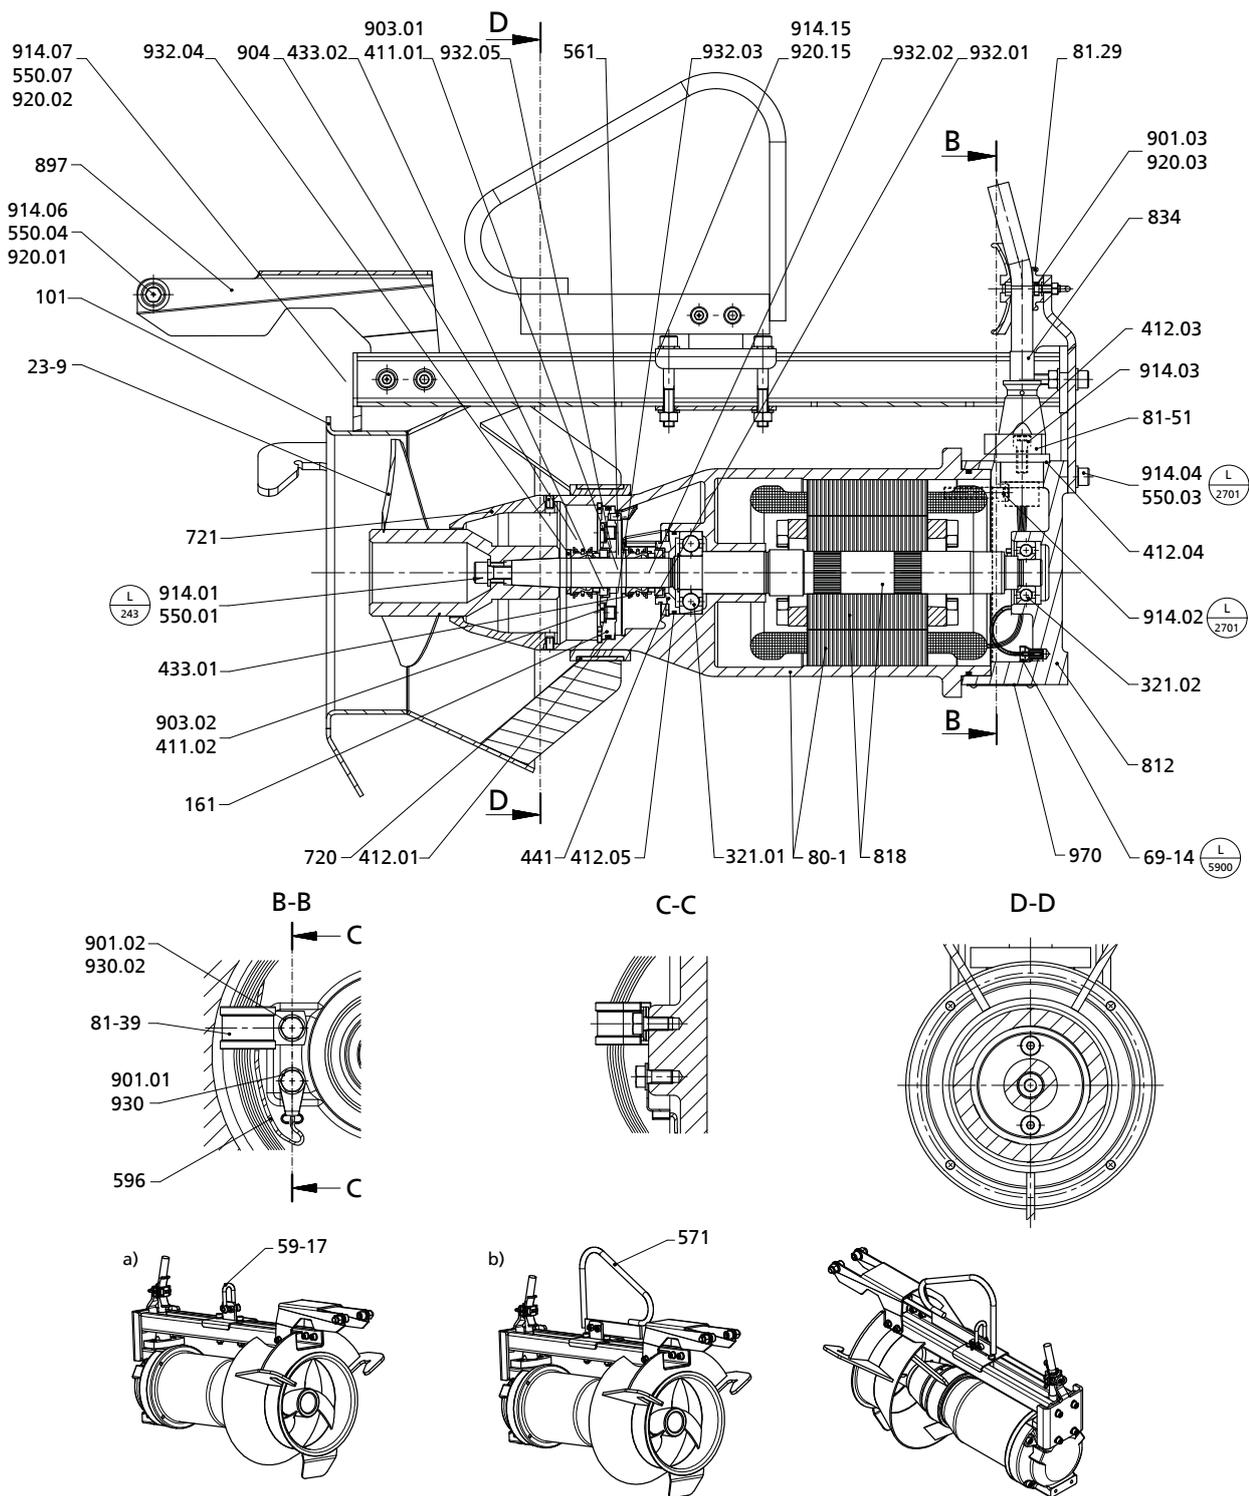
Чертеж общего вида: а) с серьгой б) со скобой (дополнительно)
